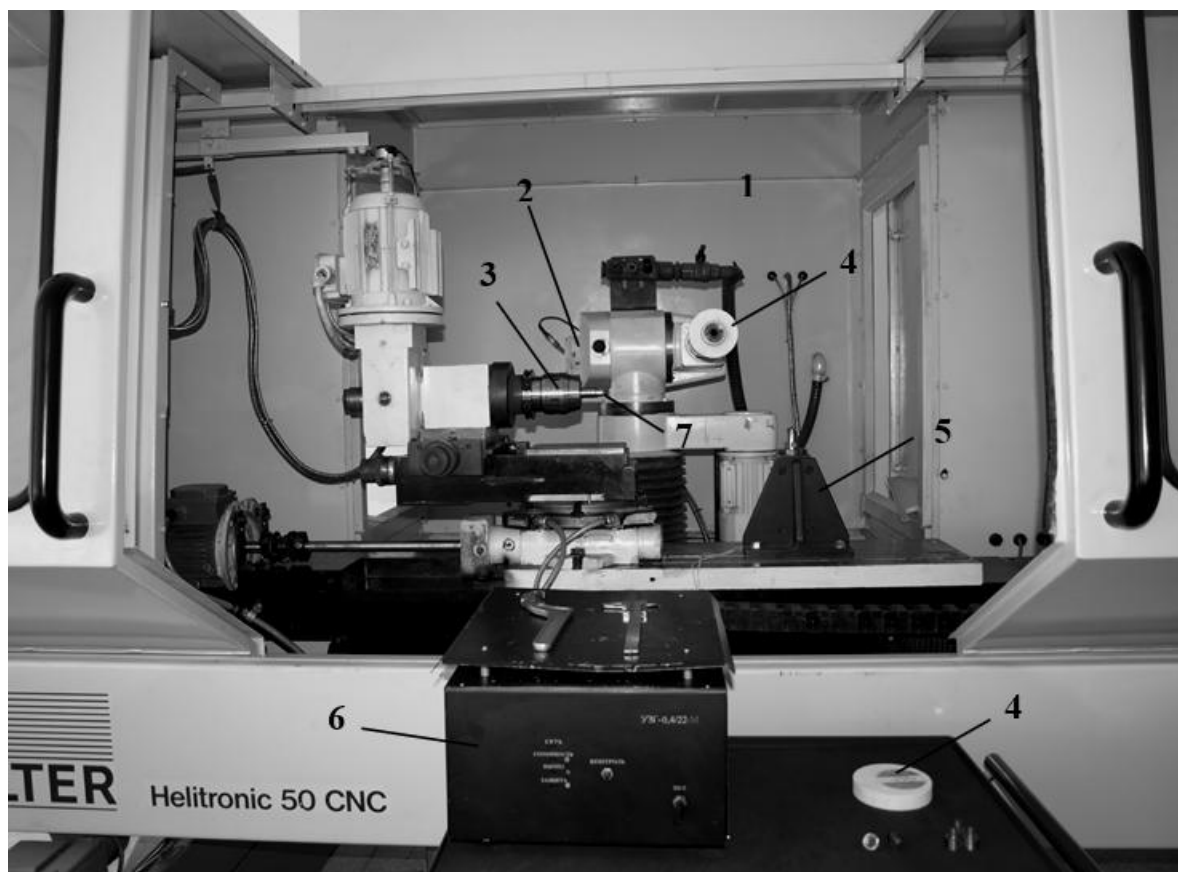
Рабочая зона шлифовально-заточного станка Walter Helitronic 50 CNC: 1 – шлифовальная бабка; 2 – привод вращения шпинделя; 3 – цанга; 4 – шлифовальный круг; 5 – устройство для ультразвуковой правки; 6 – генератор ультразвуковых колебаний; 7 – образцы для шлифования
